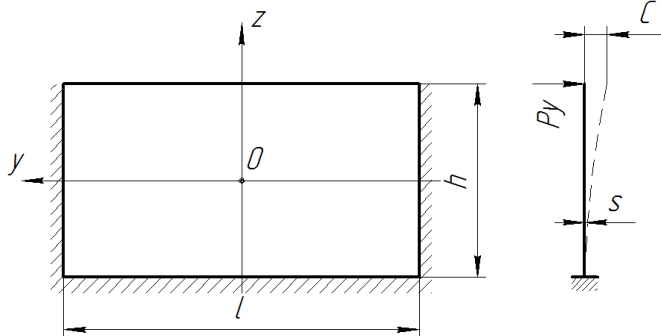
Представление обрабатываемой стенки в виде пластины.
